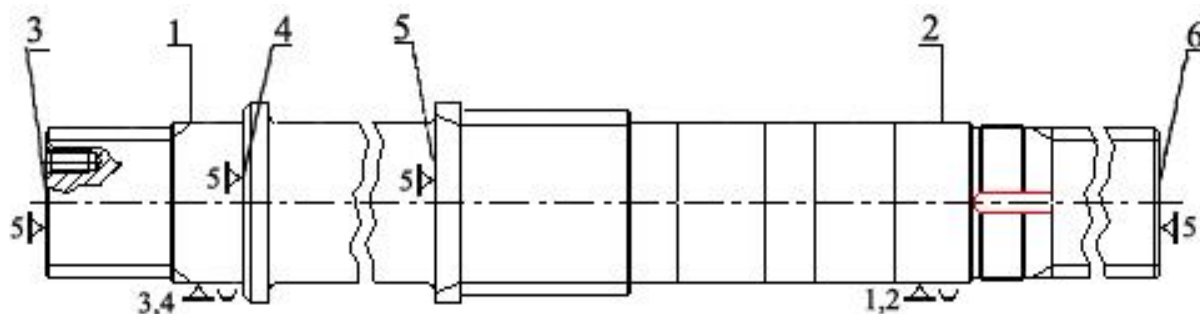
Варіанти схеми базування на фрезерній операції з ЧПК
